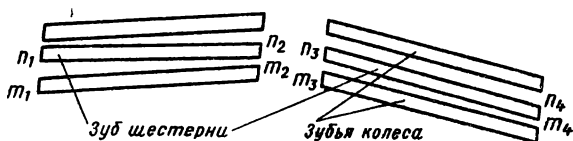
Схема расположения зубьев шестерни и колеса при центрировании
